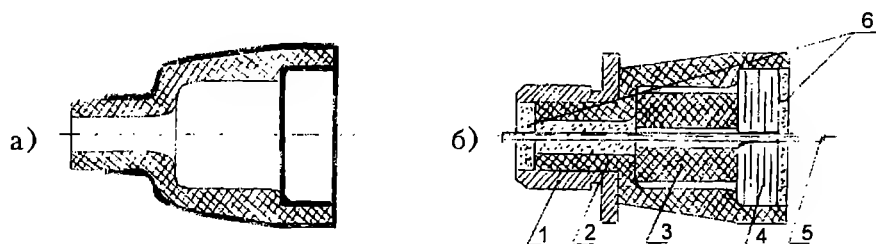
Конструкция фильтра на основе шайбового монолитного конденсатора. а) керамический корпус фильтра, б) фильтр в сборе. 1- гайка, 2 - керамический корпус, 3 - ферритовая трубка, 4 - шайбовый монолитный конденсатор, 5 - проходной стержень, 6 - заливочный компаунд
